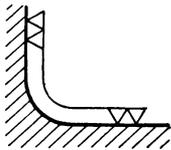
Oberflächenzeichen an gerundeten Übergängen
